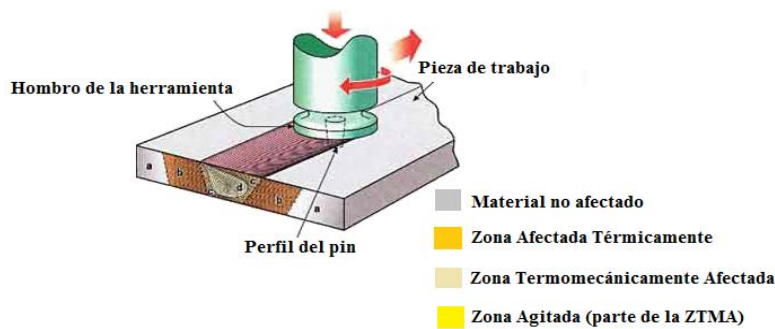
Modo de aplicación del calentamiento por fricción. Fuente: Buffa *et al.* (2006).
